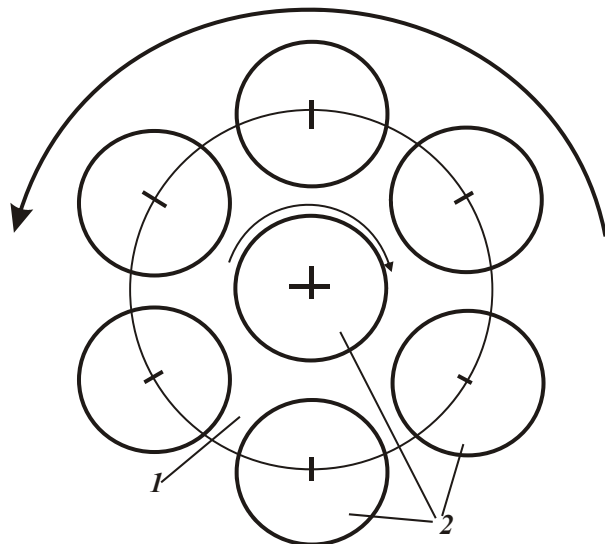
Схема шлифования чашечными или тарельчатыми кругами с кругом в центре: 1 – вращающийся несущий диск; 2 – круг.
